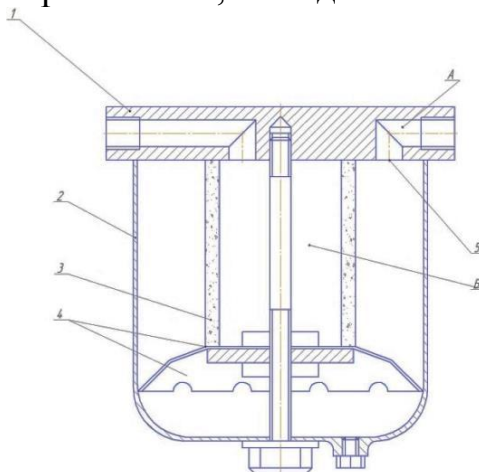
Очистка от конденсата: 1 - основание; 2 - корпус; 3 - фильтрующий керамический элемент; 4 - конус отражателя; 5 - втулка
